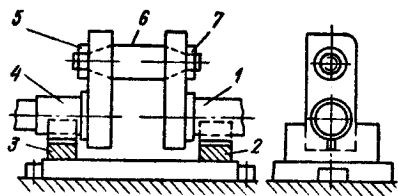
Пристрій для складання складаного колінчастого вала
